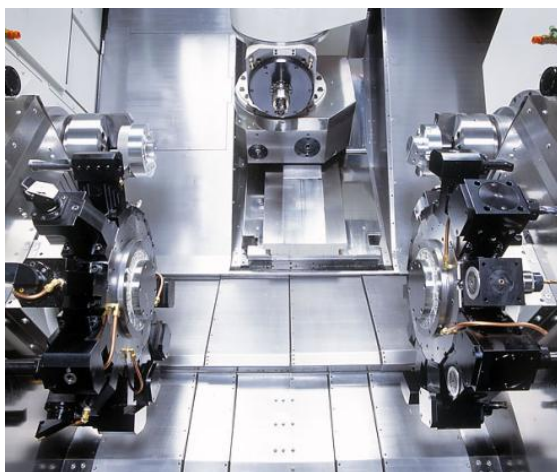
Токарно-фрезерный центр Nakamura-Tome
